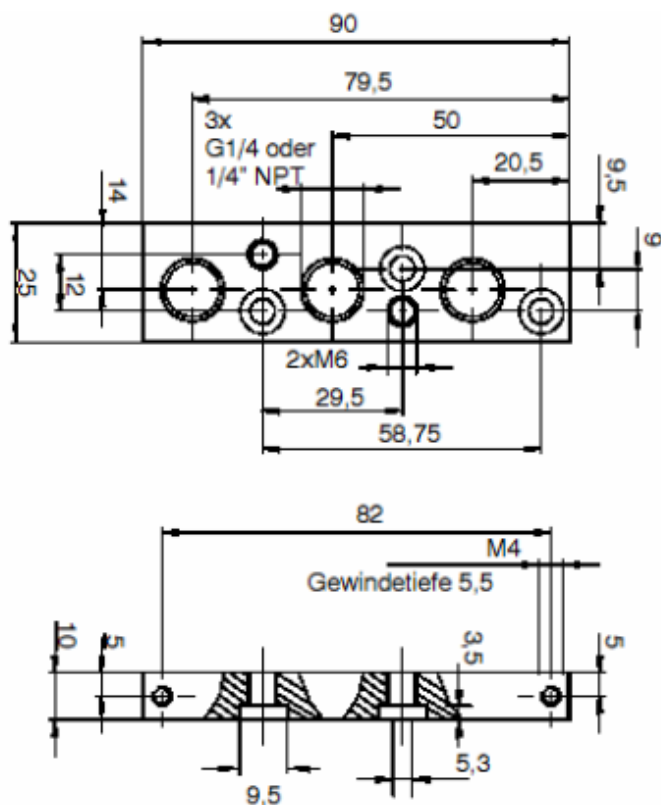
Габаритный чертеж соединительной планки для пластикового корпуса
